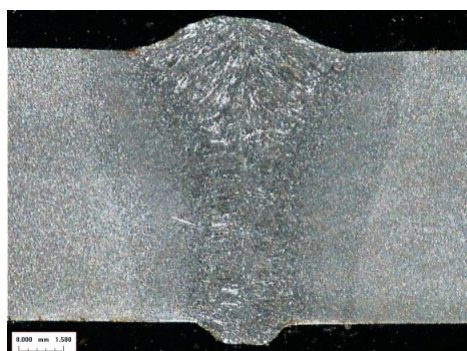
Макрошлиф сварного шва, полученного гибридным лазерно-дуговым способом сварки, толщина 10 мм
